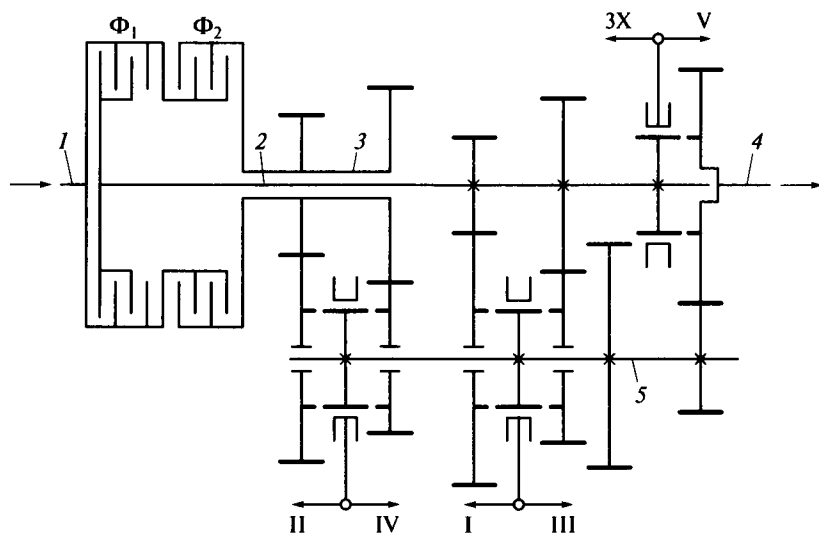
Схема коробки передач с двумя сцеплениями:
